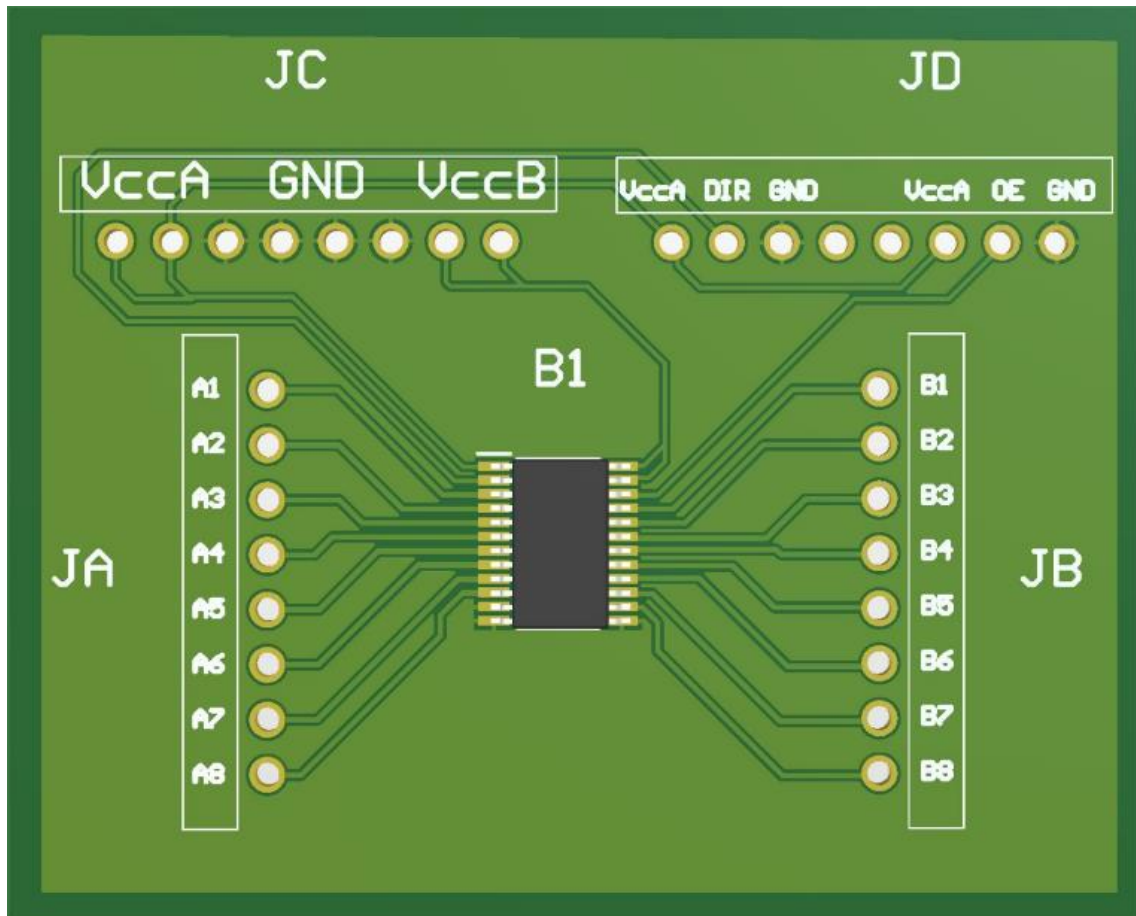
Diseño PCB del chip de adaptación de tensión.
